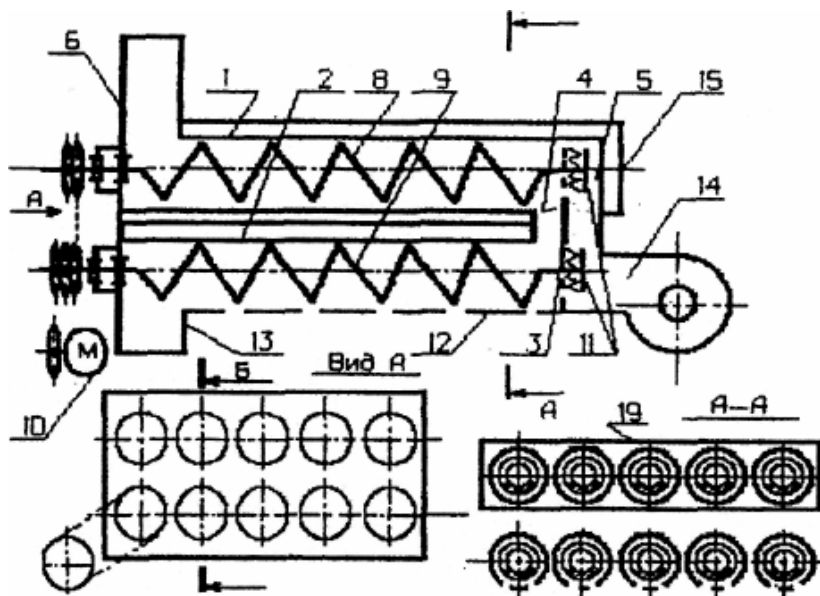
Сушилка зерна с пружинно-транспортирующим рабочим органом батарейного типа:
